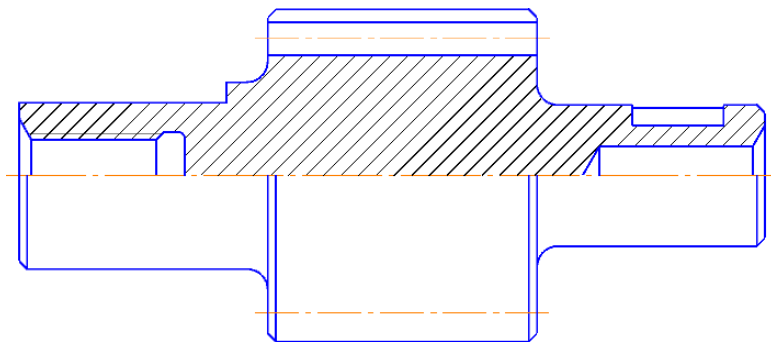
Построение метрической резьбы с проточкой для режущего инструмента с левого торца вала
